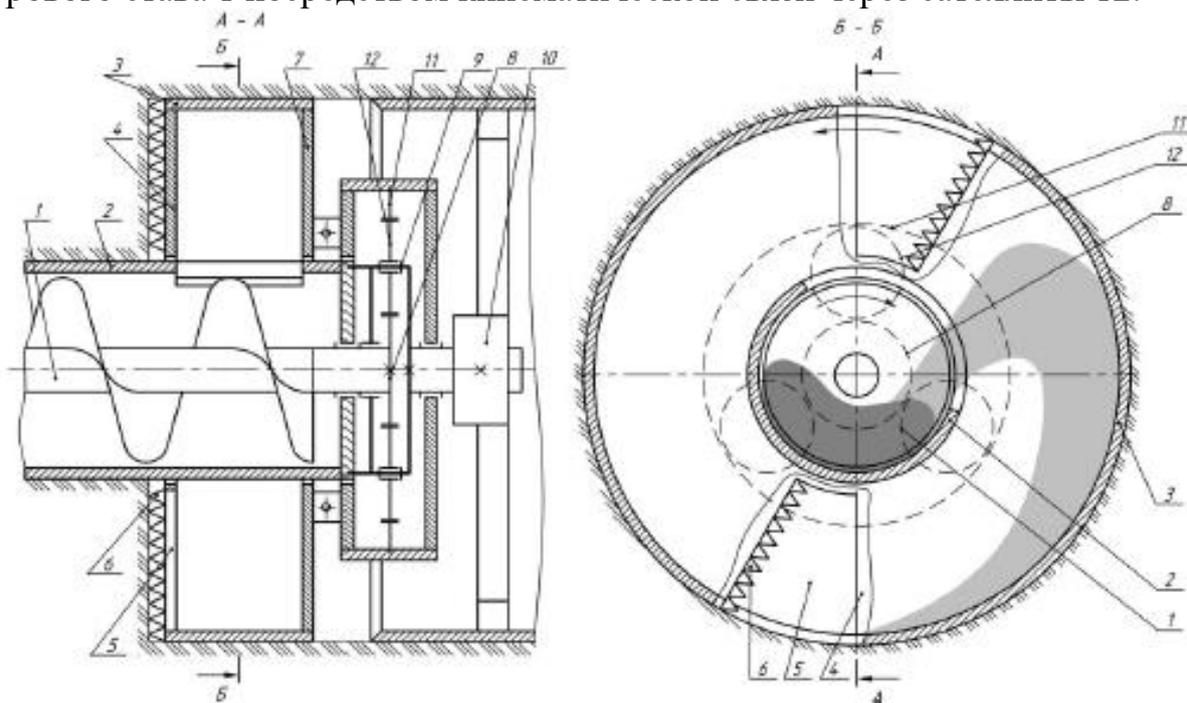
Барабанный расширитель горизонтальных скважин с планетарным редуктором и якорно-прицепным устройством
